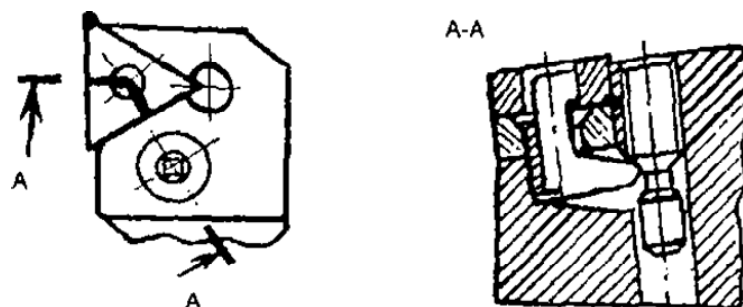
Эскизы рабочей части сборных инструментов: тип крепления РР
